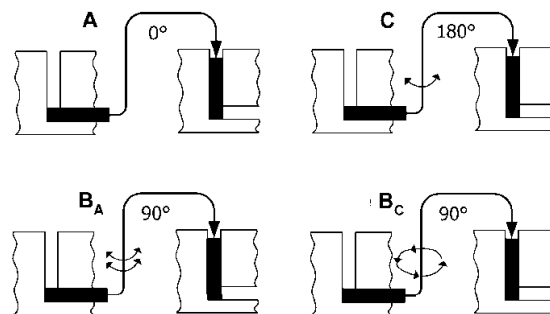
Основные маршруты РКУП прутковой заготовки.
